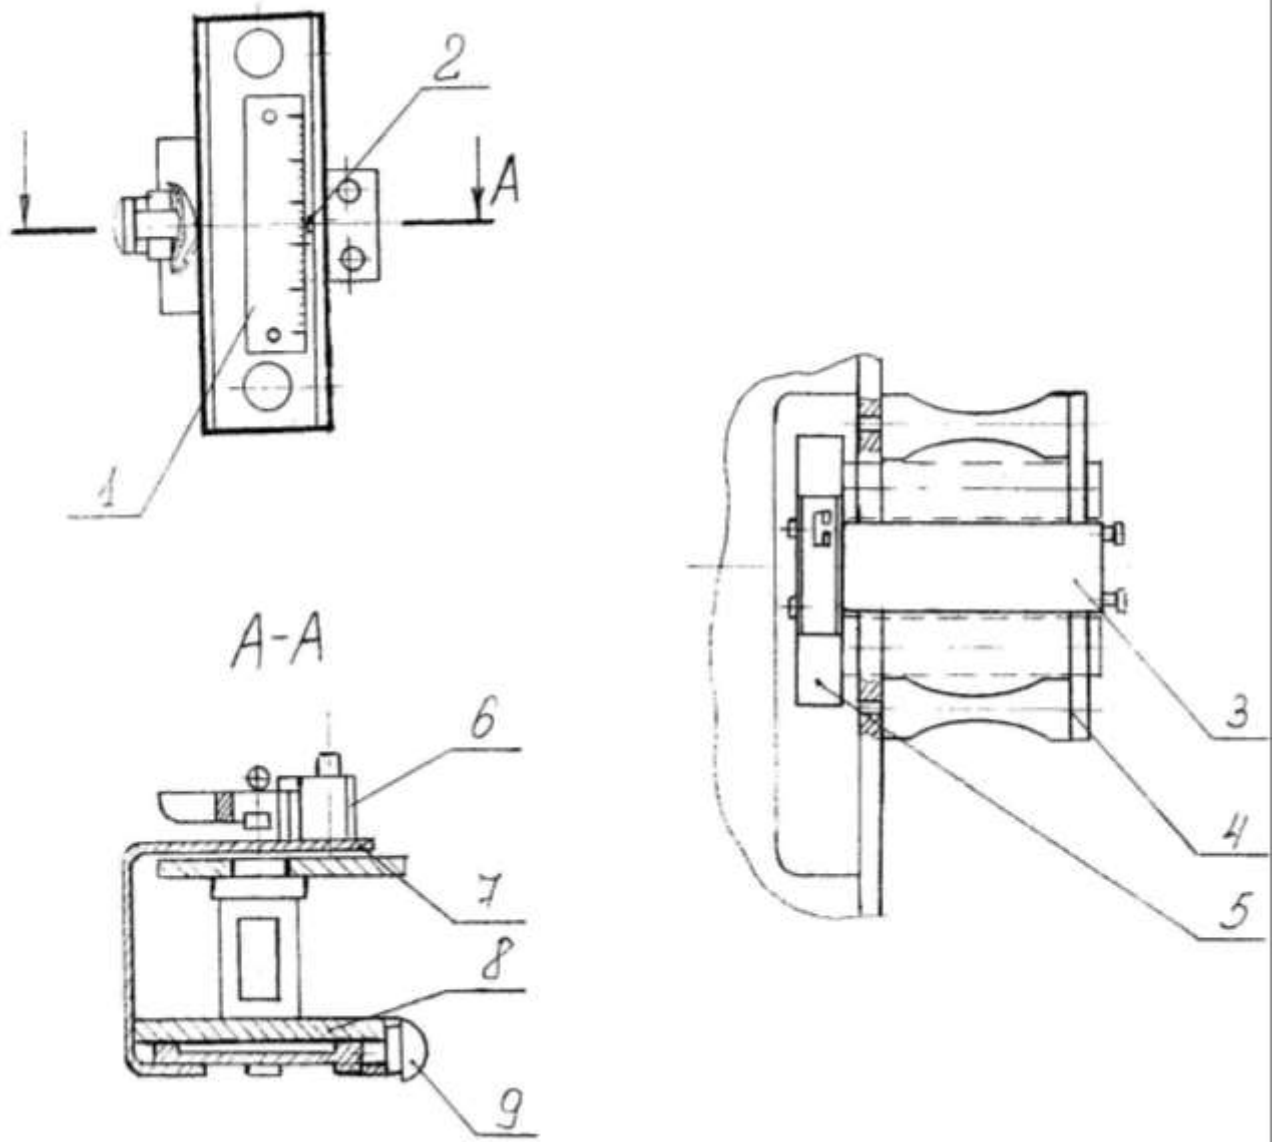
Пристрій для установки технологічного зазору преса ПГТП-45-1-О
